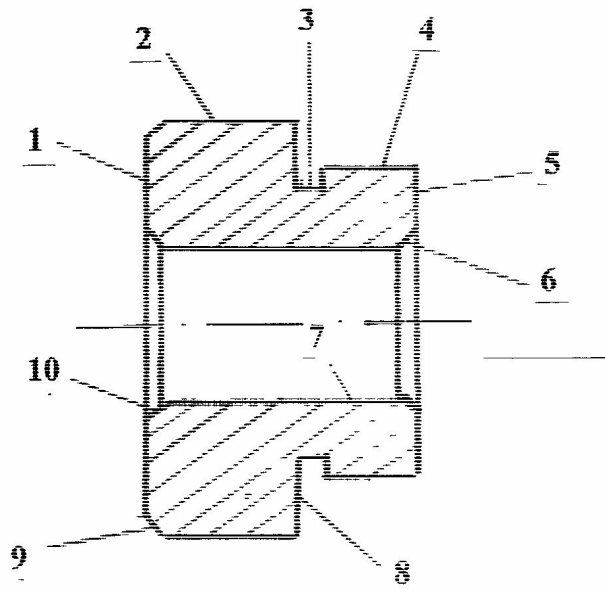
Ескіз деталі та нумерація її поверхонь
